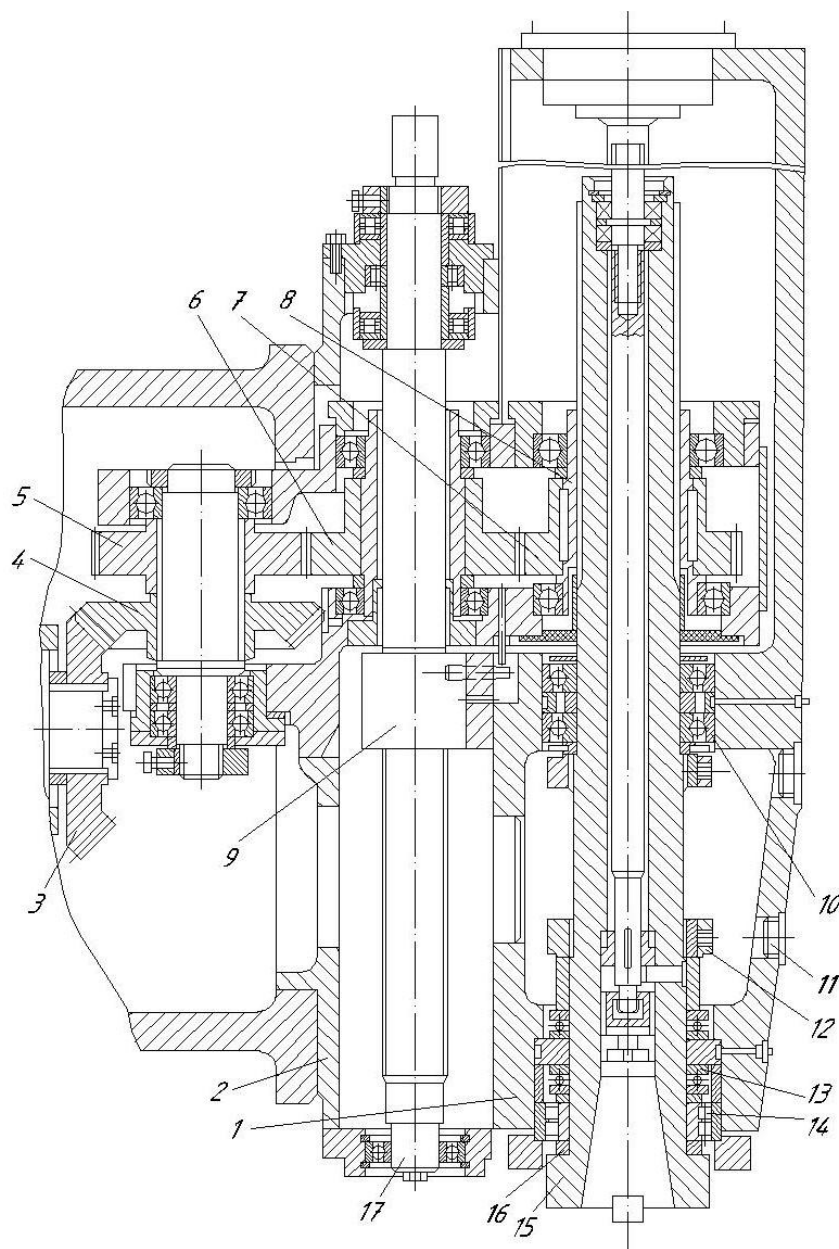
Шпиндельная бабка с ползуном вертикально-фрезерного станка с ЧПУ.
